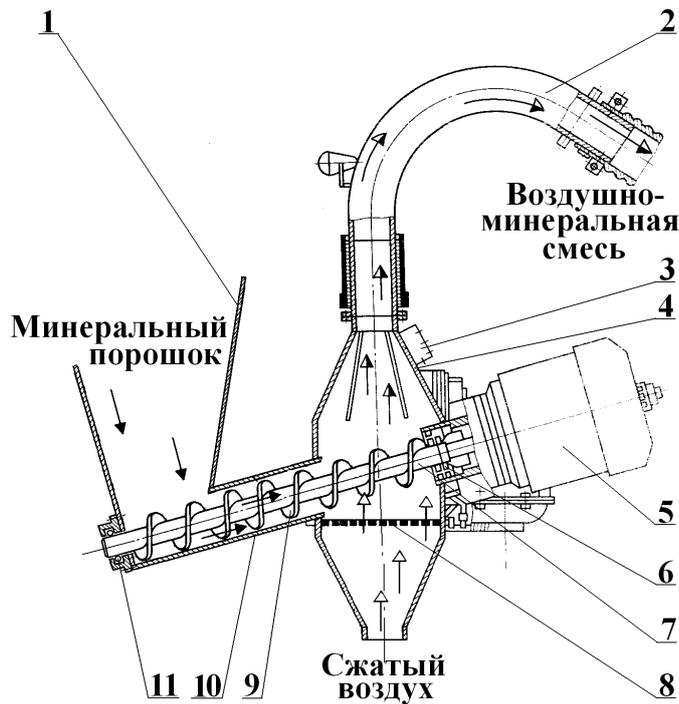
Схема устройства и работы пневмотранспортёра минерального порошка: 1 – приемный бункер; 2 – пневмопровод; 3 – вибратор сводообрушителя; 4 – смесительная камера; 5 – электропривод шнека; 6 – соединительная муфта; 7 – вал шнека; 8 – фильтр; 9 – шнек; 10 – кожух шнека; 11 – опорный подшипник шнека
